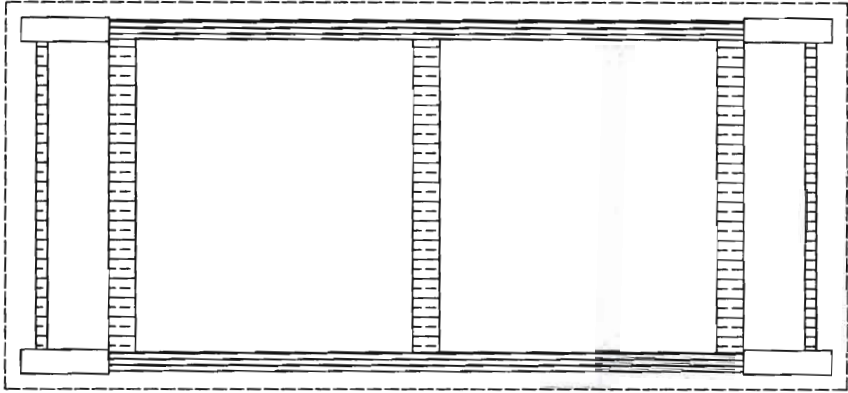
DETAIL DE LA PLANCHE DE TRAVAIL OU TOP
